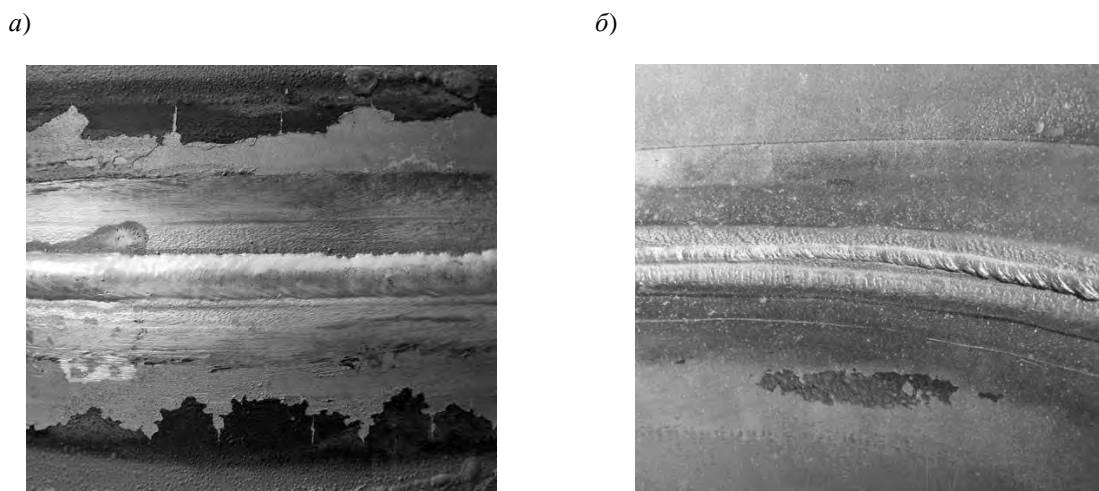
Внешний вид сварного соединения: *а* – наружная поверхность шва; *б* – внутренняя поверхность шва (по краям обратного валика наблюдаются валики заводского сварного соединения)
